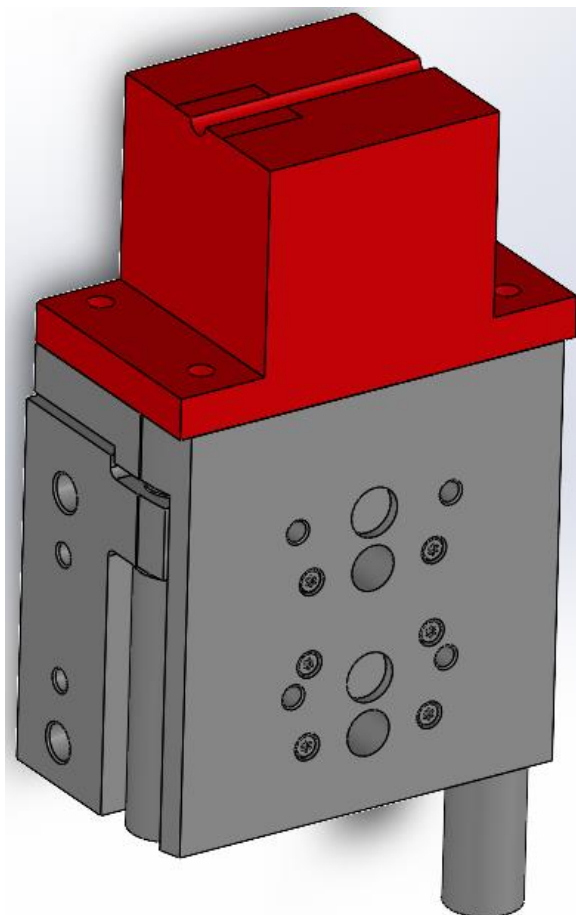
Нижний пневмоцилиндр с прижимом
